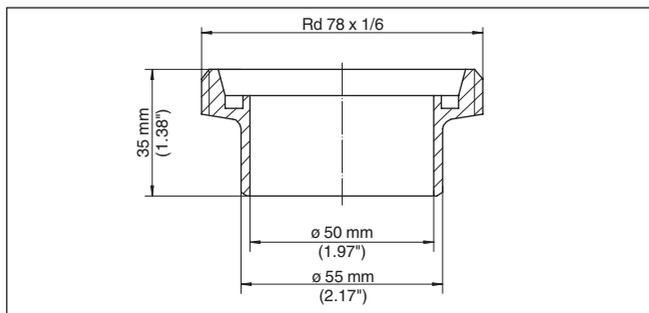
Medidas da luva para soldagem união rosçada para tubo DN 50
